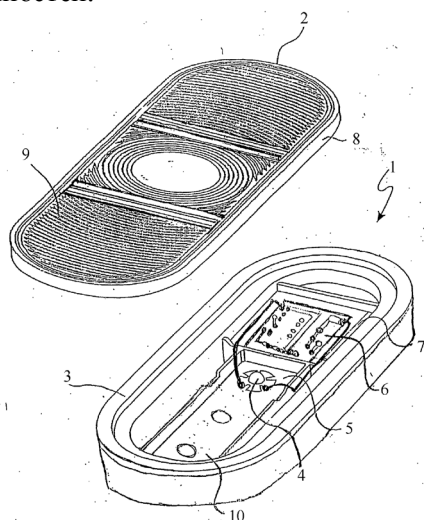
Конструкция фонаря в соответствии с патентом 03/074931A1: 1 – корпусный узел фонаря; 2 – рассеиватель; 3 – корпус; 4 – мощный светодиод; 5 – радиатор светодиода; 6 – схема питания светодиода; 7 – отсек схемы питания; 8 – участок рассеивателя для ультразвуковой сварки; 9 – периферическая оптика фонаря; 10 – место для дополнительных светодиодов
